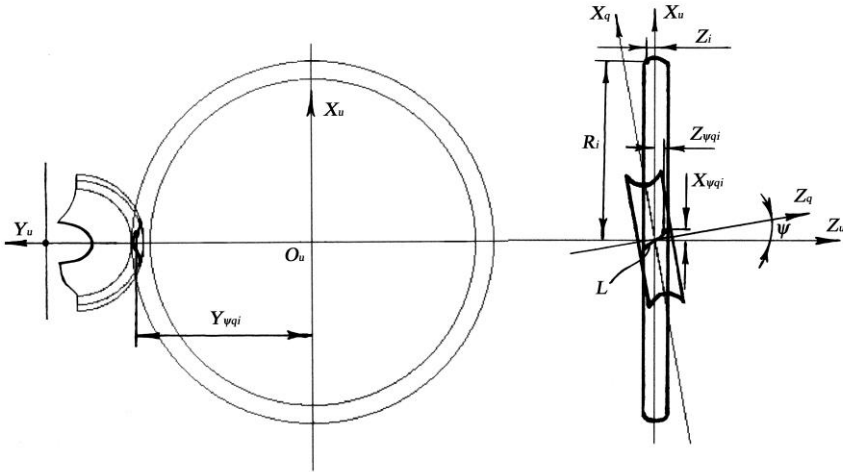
Схема определения линии контакта шлифовального круга и детали
